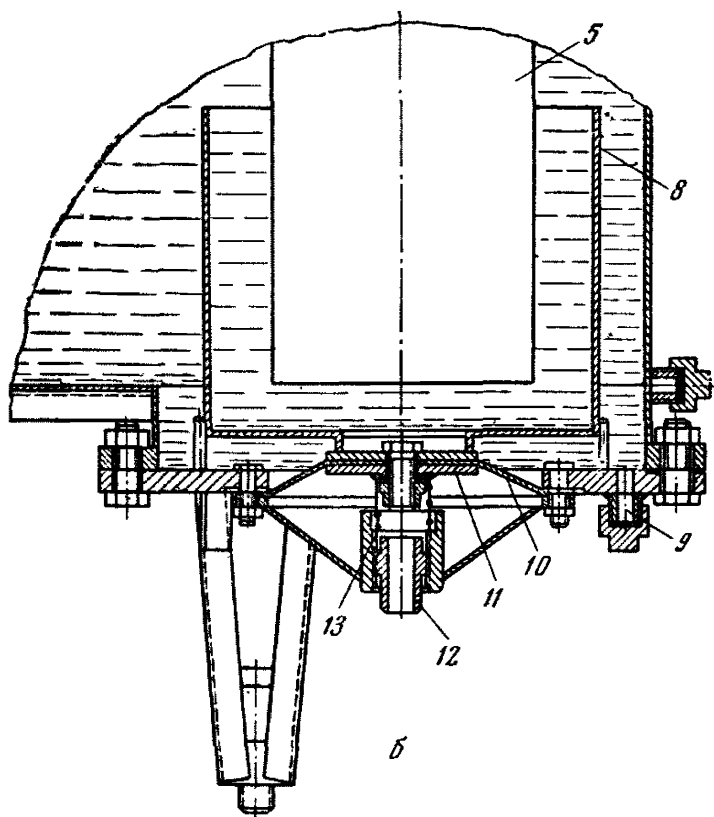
Предохранительный гидравлический клапан КПГ-150 для резервуаров с повышенным избыточным давлением:
